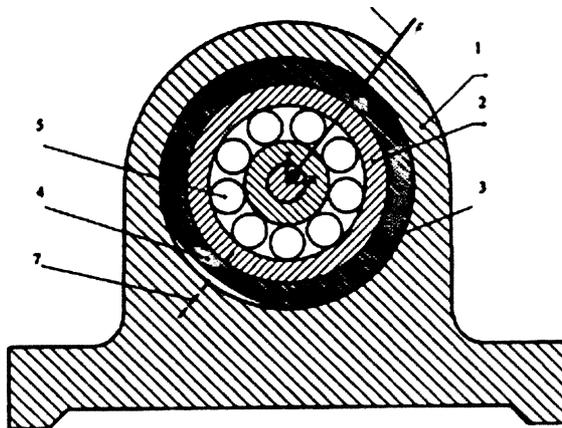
Конструкция подшипниковой опоры с переменной жесткостью
